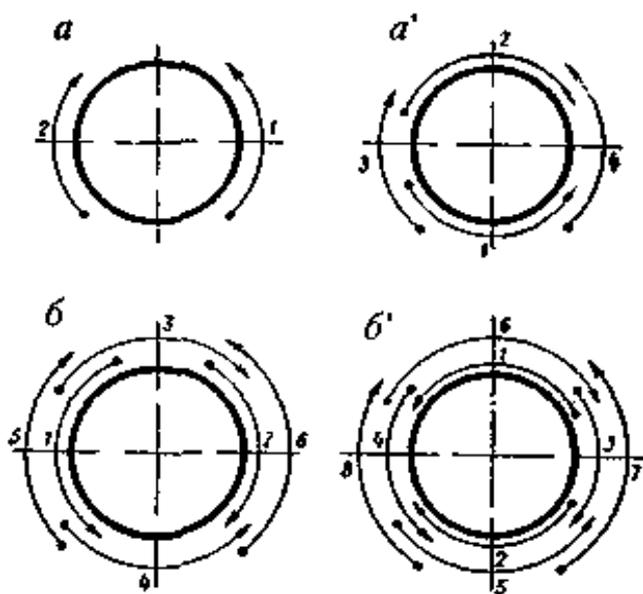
Сварка стыков с поворотом трубы на 90° :
